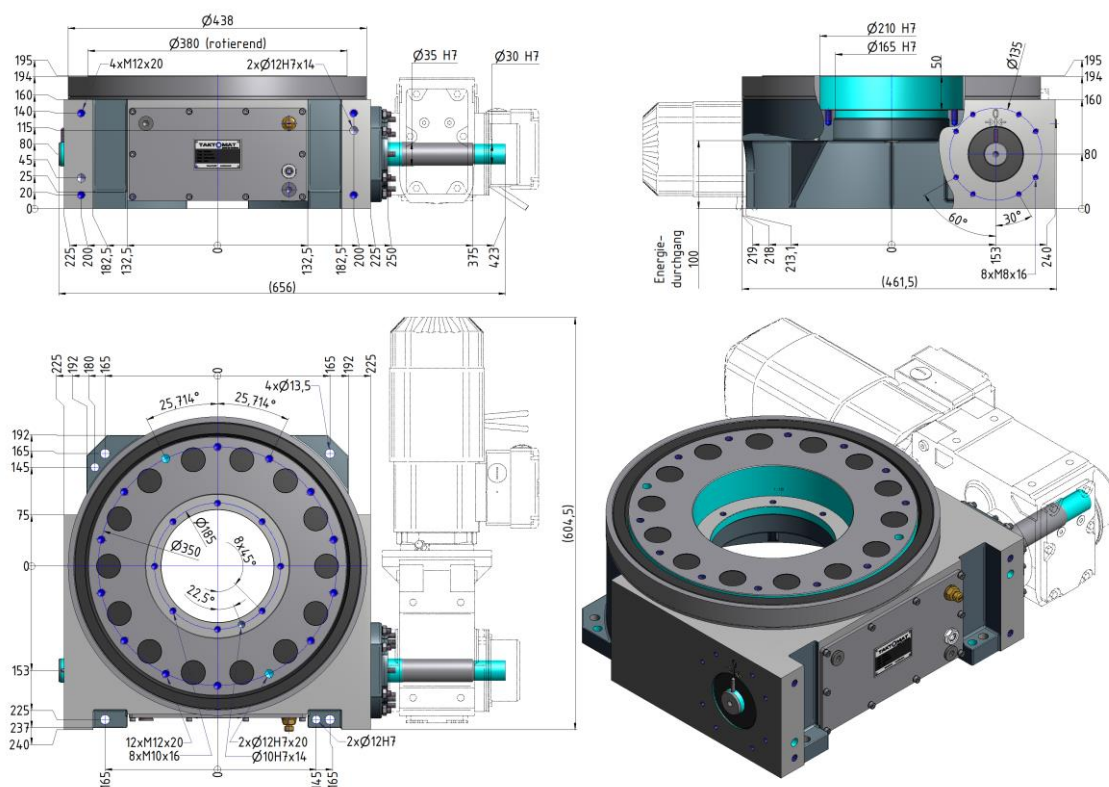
Hoja de dimensiones TMF 1000 horizontal
